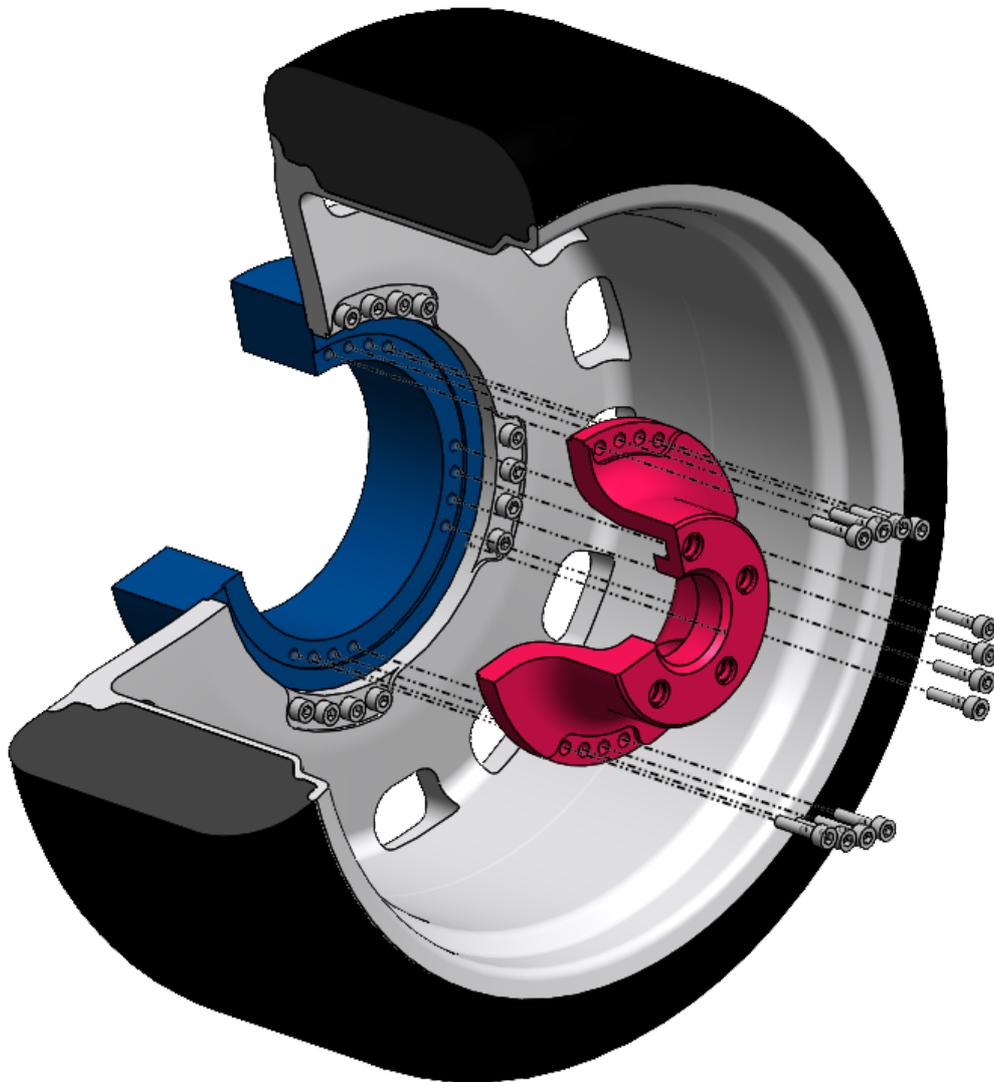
Den Nabenadapter (= Innenadapter; rot) mit dem WFT (blau) verschrauben.
